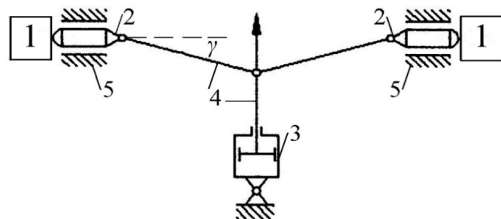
Схема нагружения маложесткого кольца I плунжерами 2 в устройстве по [11]: 3 – гидропривод; 4 – рычажно-шарнирный механизм; 5 – корпус; γ – угол наклона рычага
